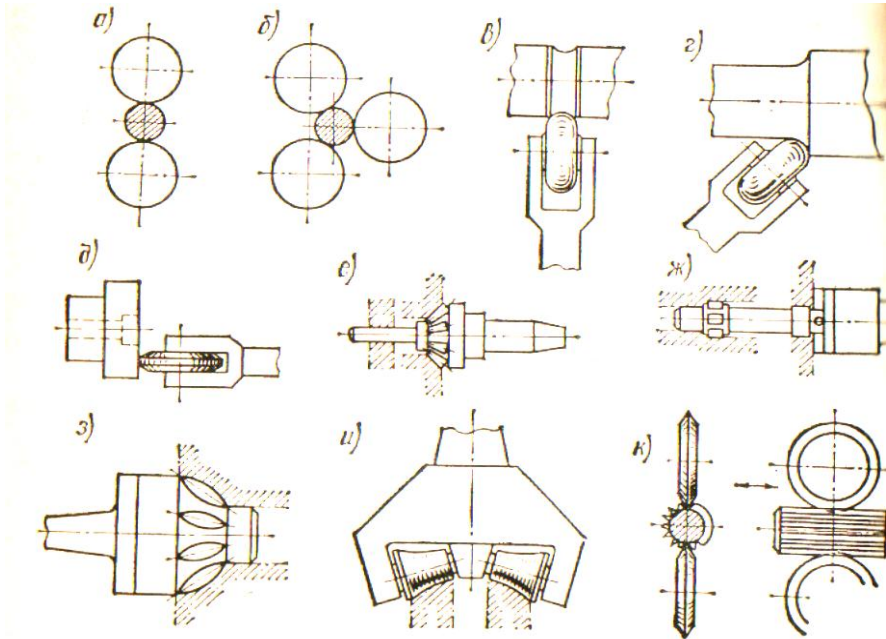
Схемы обкатки поверхностей гладкими роликами
